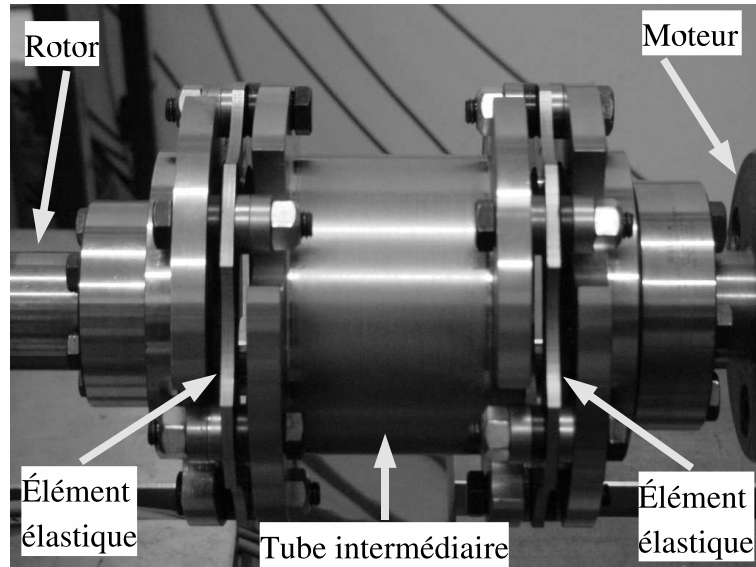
Le joint d'accouplement de type "double cardan"
